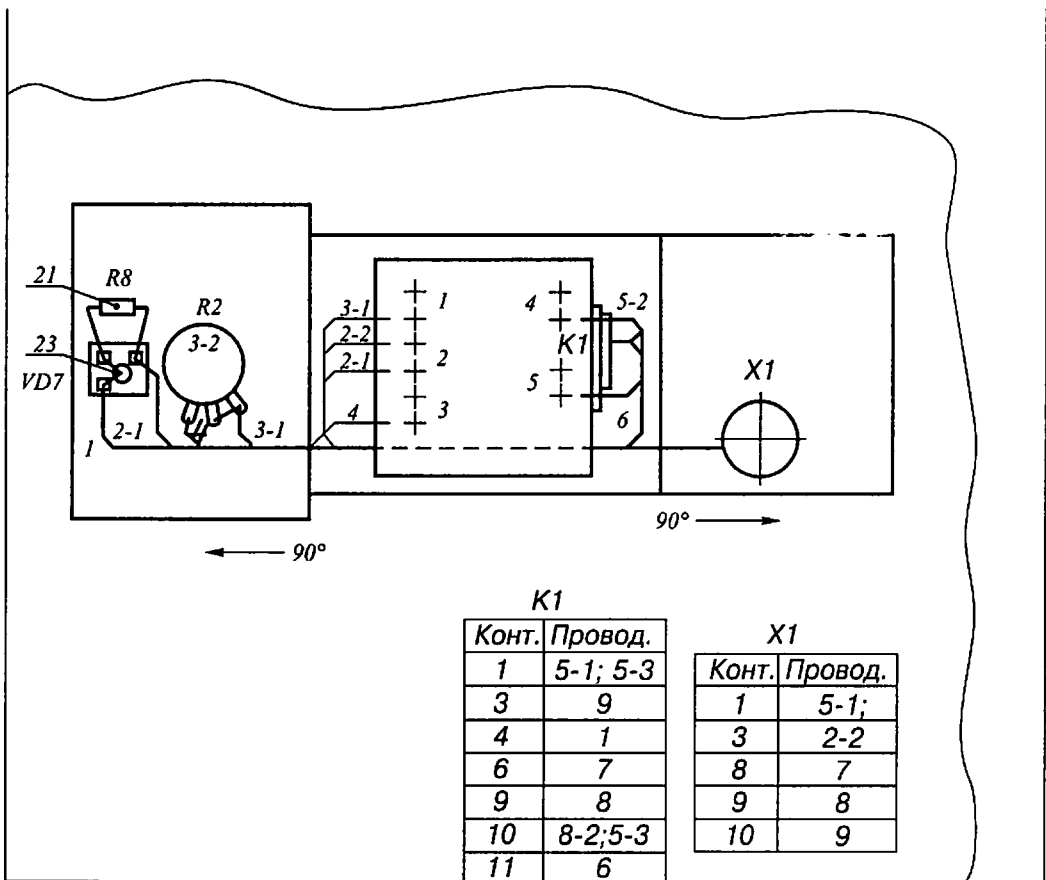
Електромонтажний кресленик (фрагмент)
